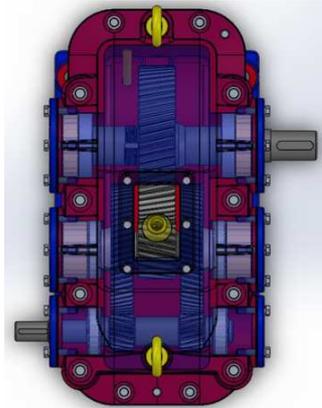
Вид сверху (верхняя крышка корпуса прозрачна)
